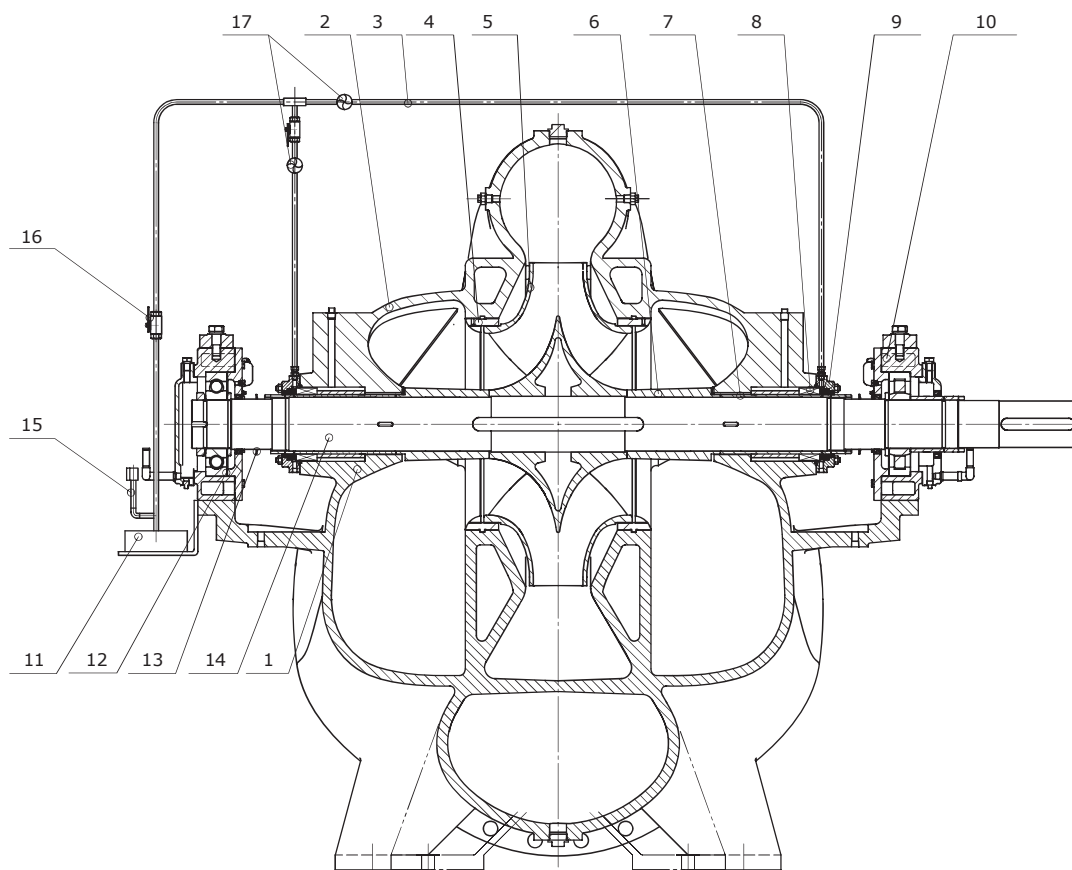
Вид в разрезе, стандартный тип исполнения 6
